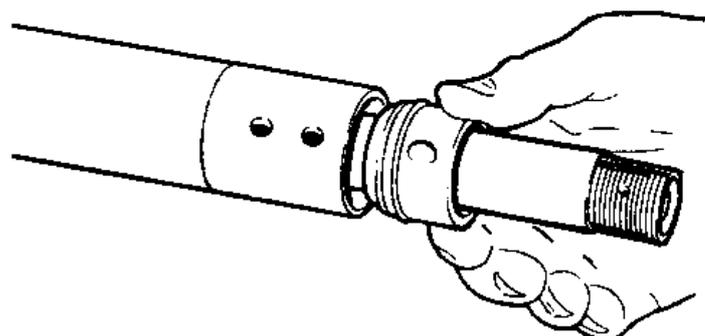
Снимите опорный подшипник рейки (Разд.35)
